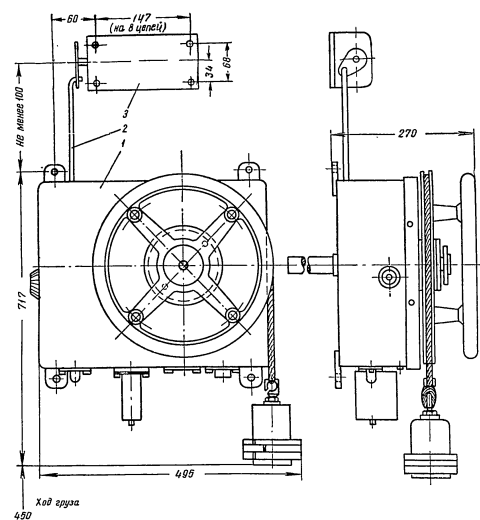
Установка блокконтактов КСА к грузовому приводу типа ПГ-10 для выключателей:
